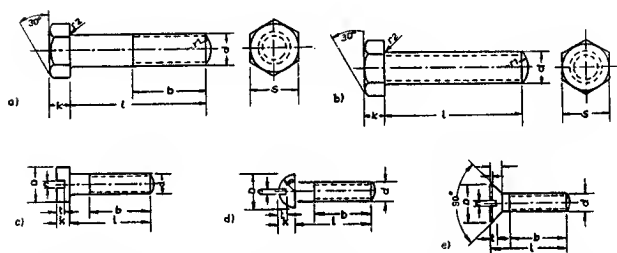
a) Sechskantschraube nach DIN 931; b) Sechskantschraube nach DIN 933; c) Zylinderschraube nach DIN 84; d) Halbrundschraube nach DIN 86; Senkschraube nach DIN 87
